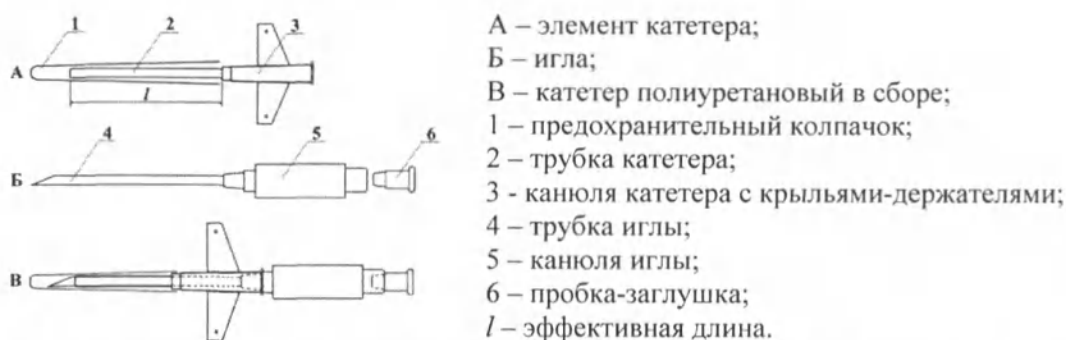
Схематическое изображение конструкции катетера полиуретанового типа 1 и 2
